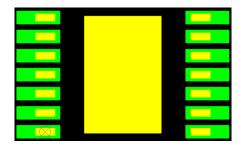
PWP0014L PCB パッドの SO-14、黄: その他の SO-14 リード、緑: TI PWP0014L PCB パッド
